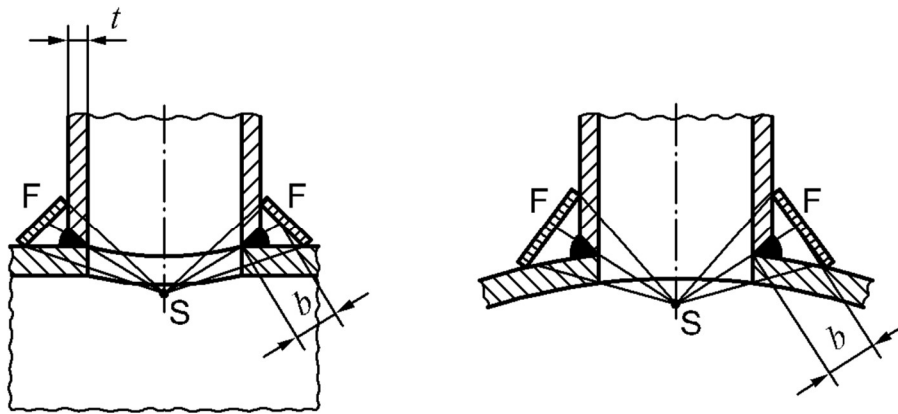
Схема контроля сварных швов наложенных деталей с источником излучения, расположенным на центральной оси трубы перпендикулярно центру сварного шва и пленкой снаружи
